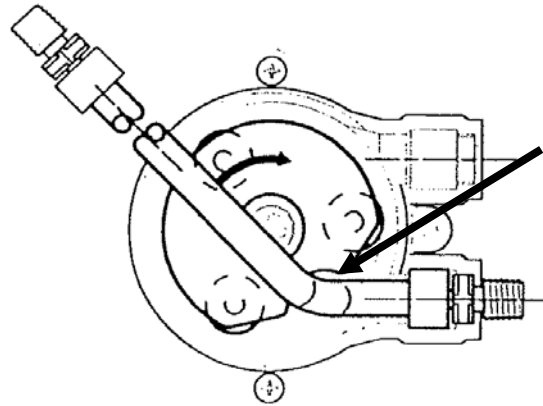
Tête de pompe / Assemblage rotor retiré
